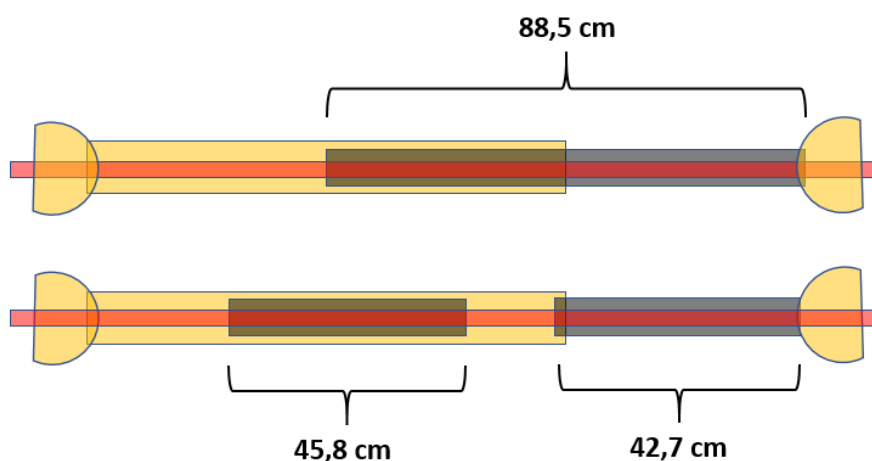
Croquis de la dimension de la section noire avant et après le sectionnement (Source : CNESST)
